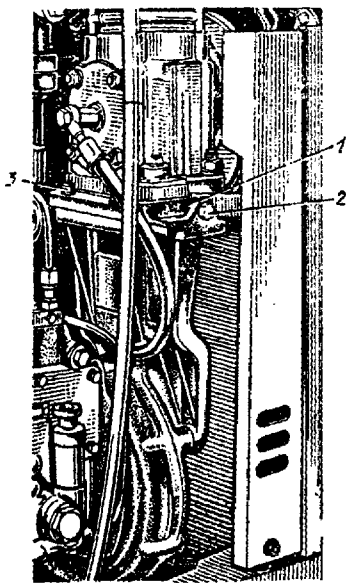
Устройство для натяжения ремня привода компрессора: 1 – гайка; 2 – натяжной болт; 3 – болт крепления
